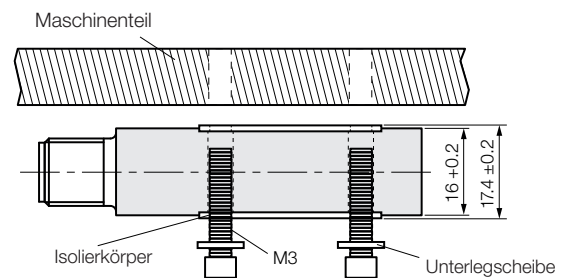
Sensorkopf mit Isolierkörper montieren
